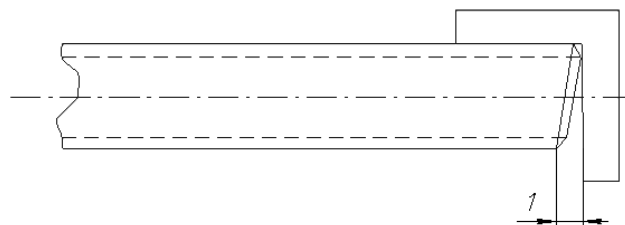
Контроль розмірів трубчатих заготовок
